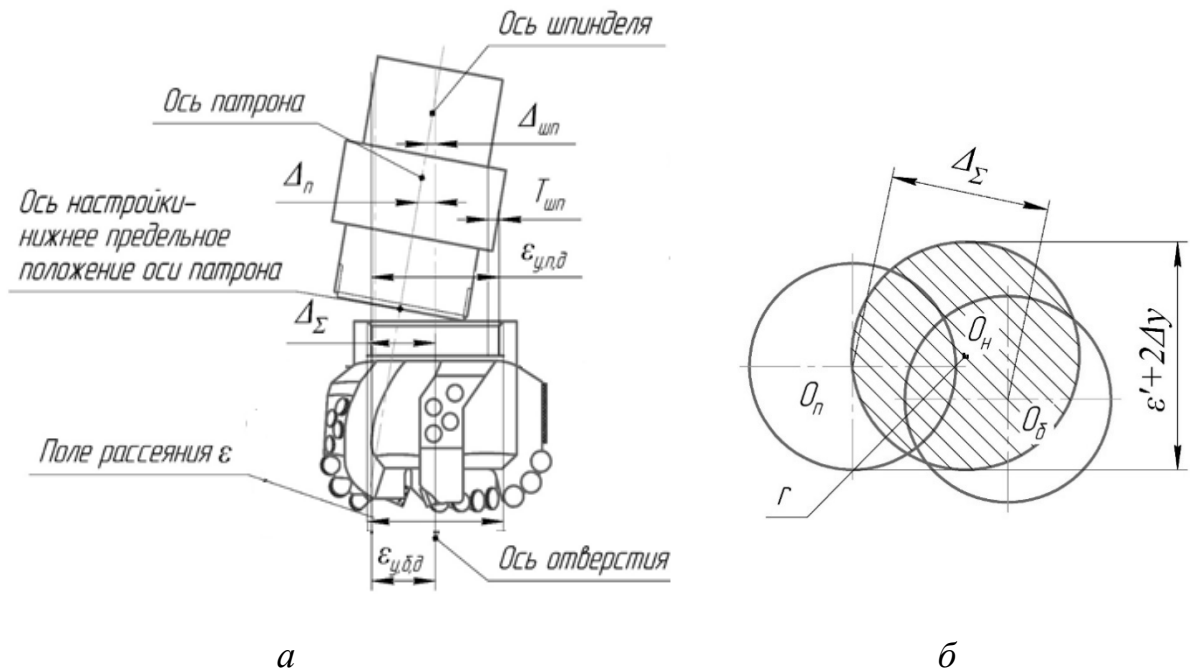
Формируемые погрешности относительного положения резьбовых поверхностей деталей при автоматической сборке: *а* – общий вид; *б* - контур перемещения торца ниппеля (присоединяемой детали O_n) перед началом сопряжения с резьбовой поверхностью корпуса ($O_б$)
